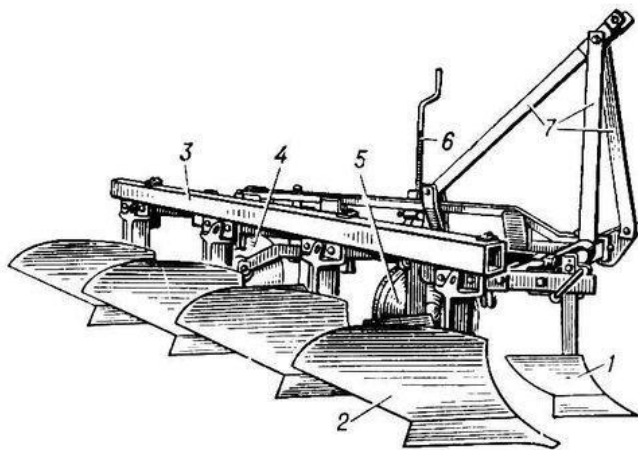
Схема плуга і встановлення його робочих органів: 1 – передплужник; 2 – корпус; 3 – рама; 4 – грудки; 5 – опорне колесо; 6 – гвинтовий механізм регулювання глибини оранки; 7 – навішування плуга [3]
